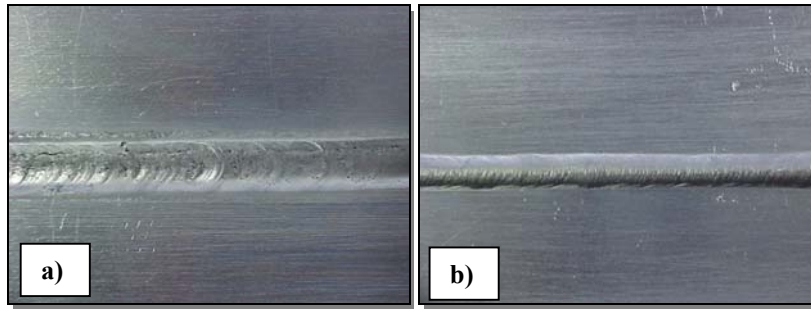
Aspecto do cordão de solda. a) Parte superior; b) raiz.
